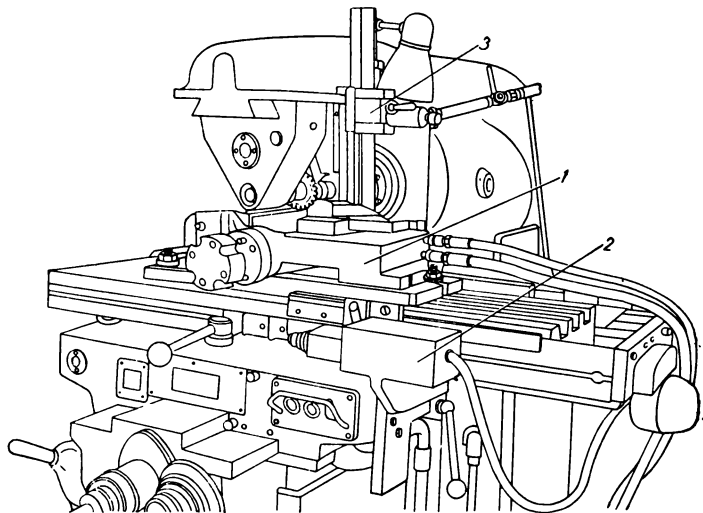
Автоматизированный консольно-фрезерный станок 6H82Г с загрузочным устройством
